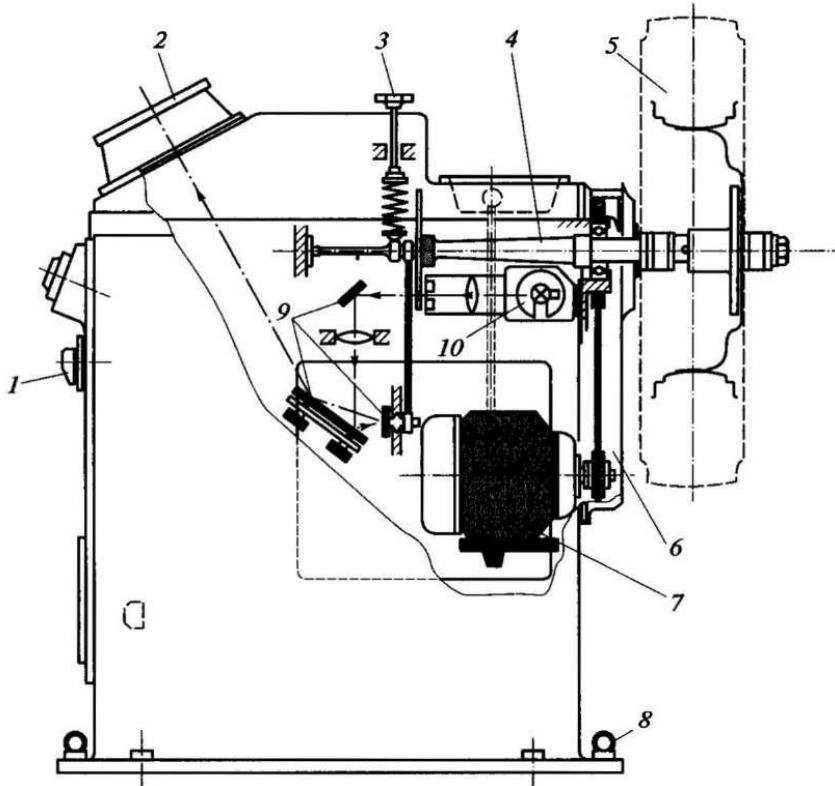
Стенд для балансировки колес, снятых с автомобиля: 1 — выключатель станка; 2 — экран станка; 3 — регулировочный винт; 4 — балансировочный вал; 5 — колесо, снятое с автомобиля; 6 — ремни привода станка; 7 — электромотор привода; 8 — транспортные рым-болты; 9 — зеркала, направляющие отклоненный луч на экран; 10 — источник света
